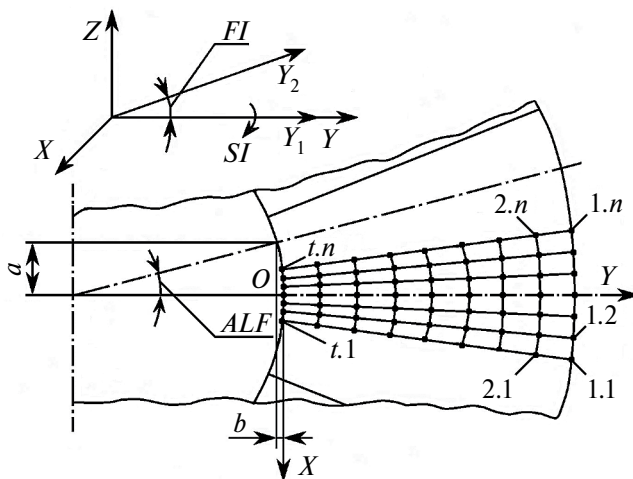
Вид сверху на схему разбивки поверхности лепестка складного зеркала параболической антенны в раскрытом положении.
